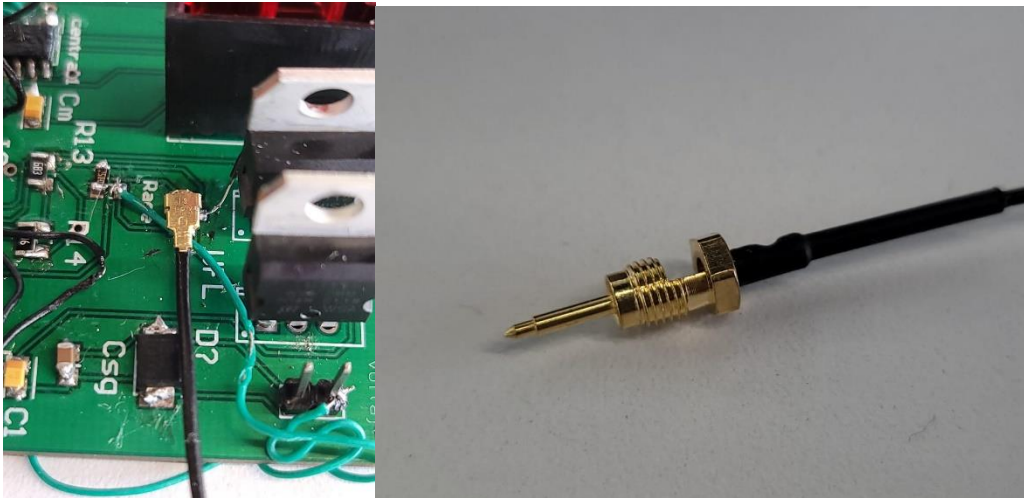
montaje en PCB conector UFL a sensor acelerómetro.
